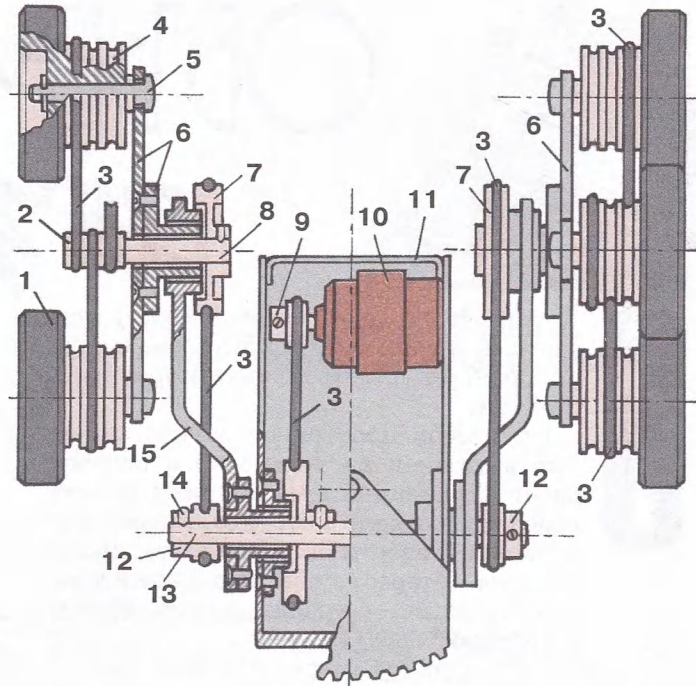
Конструкция и основные элементы модели: 1 — колесо; 2 — ведущий шкив рабочей оси; 3 — пассик; 4 — шкив колеса; 5 — ось колеса; 6 — ступица трехколесного блока; 7 — ведомый шкив рабочей оси; 8 — рабочий вал; 9 — шкив электромотора; 10 — электромотор; 11 — корпус секции модели; 12 — промежуточные шкивы распредела; 13 — ось распредела; 14 — контрольный винт шкива; 15 — подвеска блока колес.
